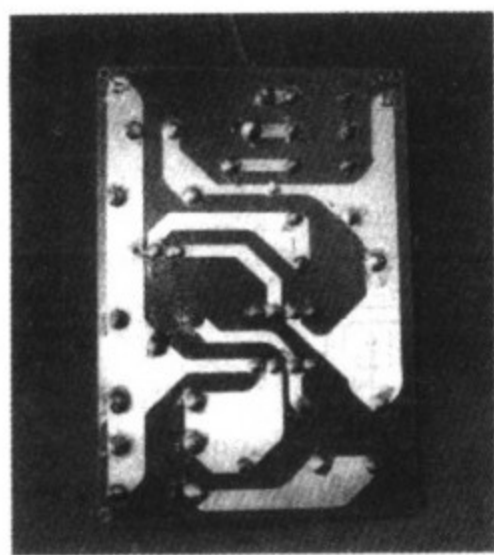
将元器件引脚焊接在 PCB 上
